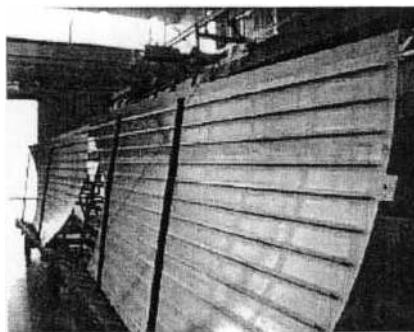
Сварные ребристые панели из листов шириной 2600 мм сплава 1424, изготовленные методом лазерной сварки на фирме «Airbus» [4]
